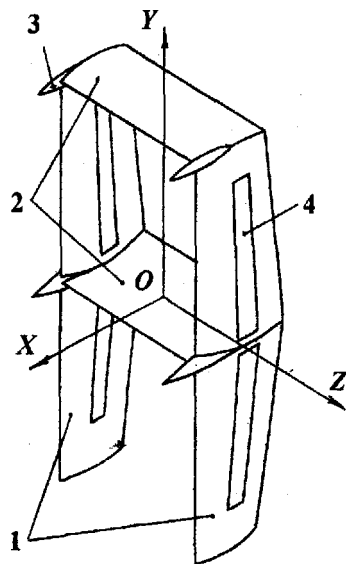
Загальний вигляд тягового біпланового модуля вітроколеса:
